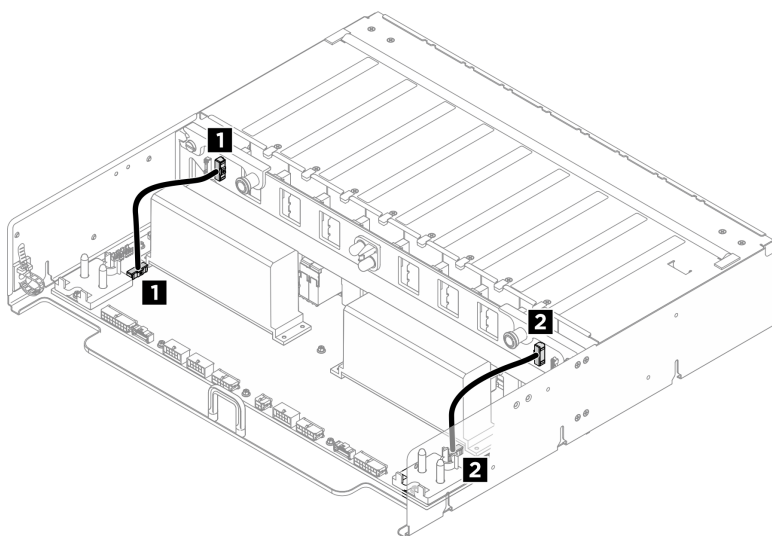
Instradamento dei cavi dall'interposer PSU alla scheda di distribuzione dell'alimentazione
